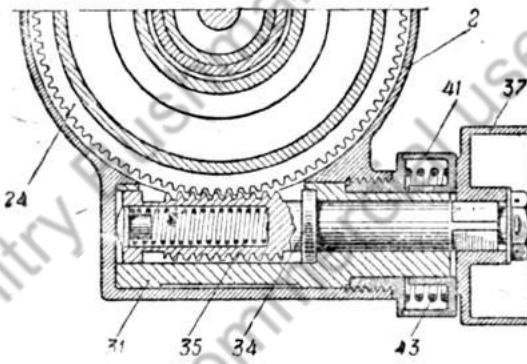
Вертикальный разрез по оси червяка подъемного механизма прицела:
